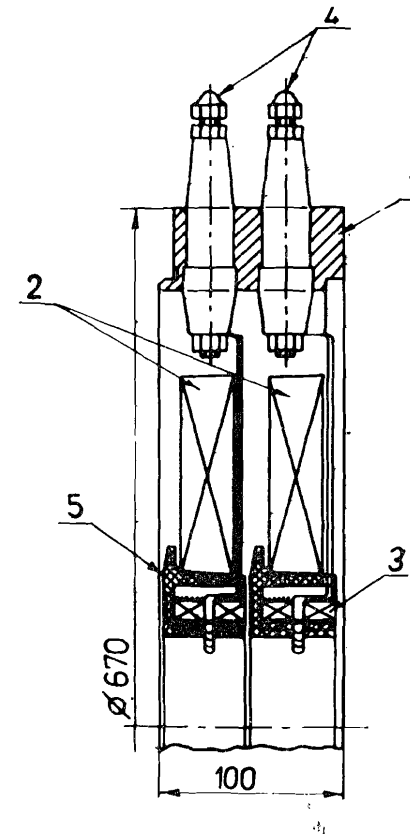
Конструкция индуктора: 1 - корпус; 2 - пермаллоевые сердечники; 3 - катушки; 4 - высоковольтные изоляторы; 5 - капролоновая обойма.
